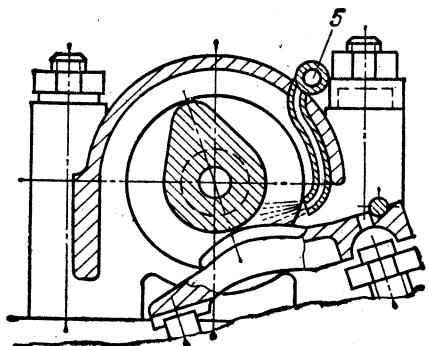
Подача масла в системе В. М. Заворотко и Э. М. Кожухова: 1 — маслоподводящий канал; 2 — центральная шпилька крепления корпуса подшипников распределителя; 3 — распределитель; 4 — корпус подшипников; 5 — маслоподводящая трубка
